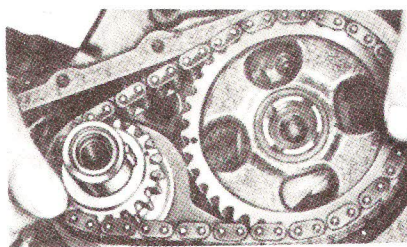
Desmontaje de Cadena y Engranaje de Sincronización. Típico
